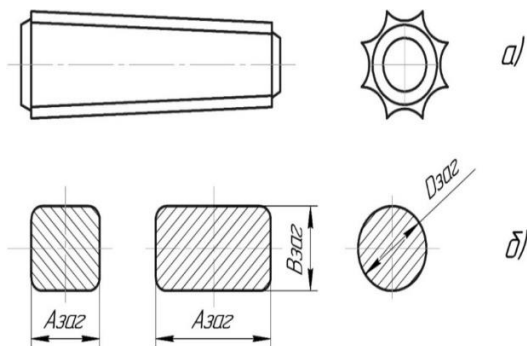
Металл, применяемый при ковке в качестве заготовок:
